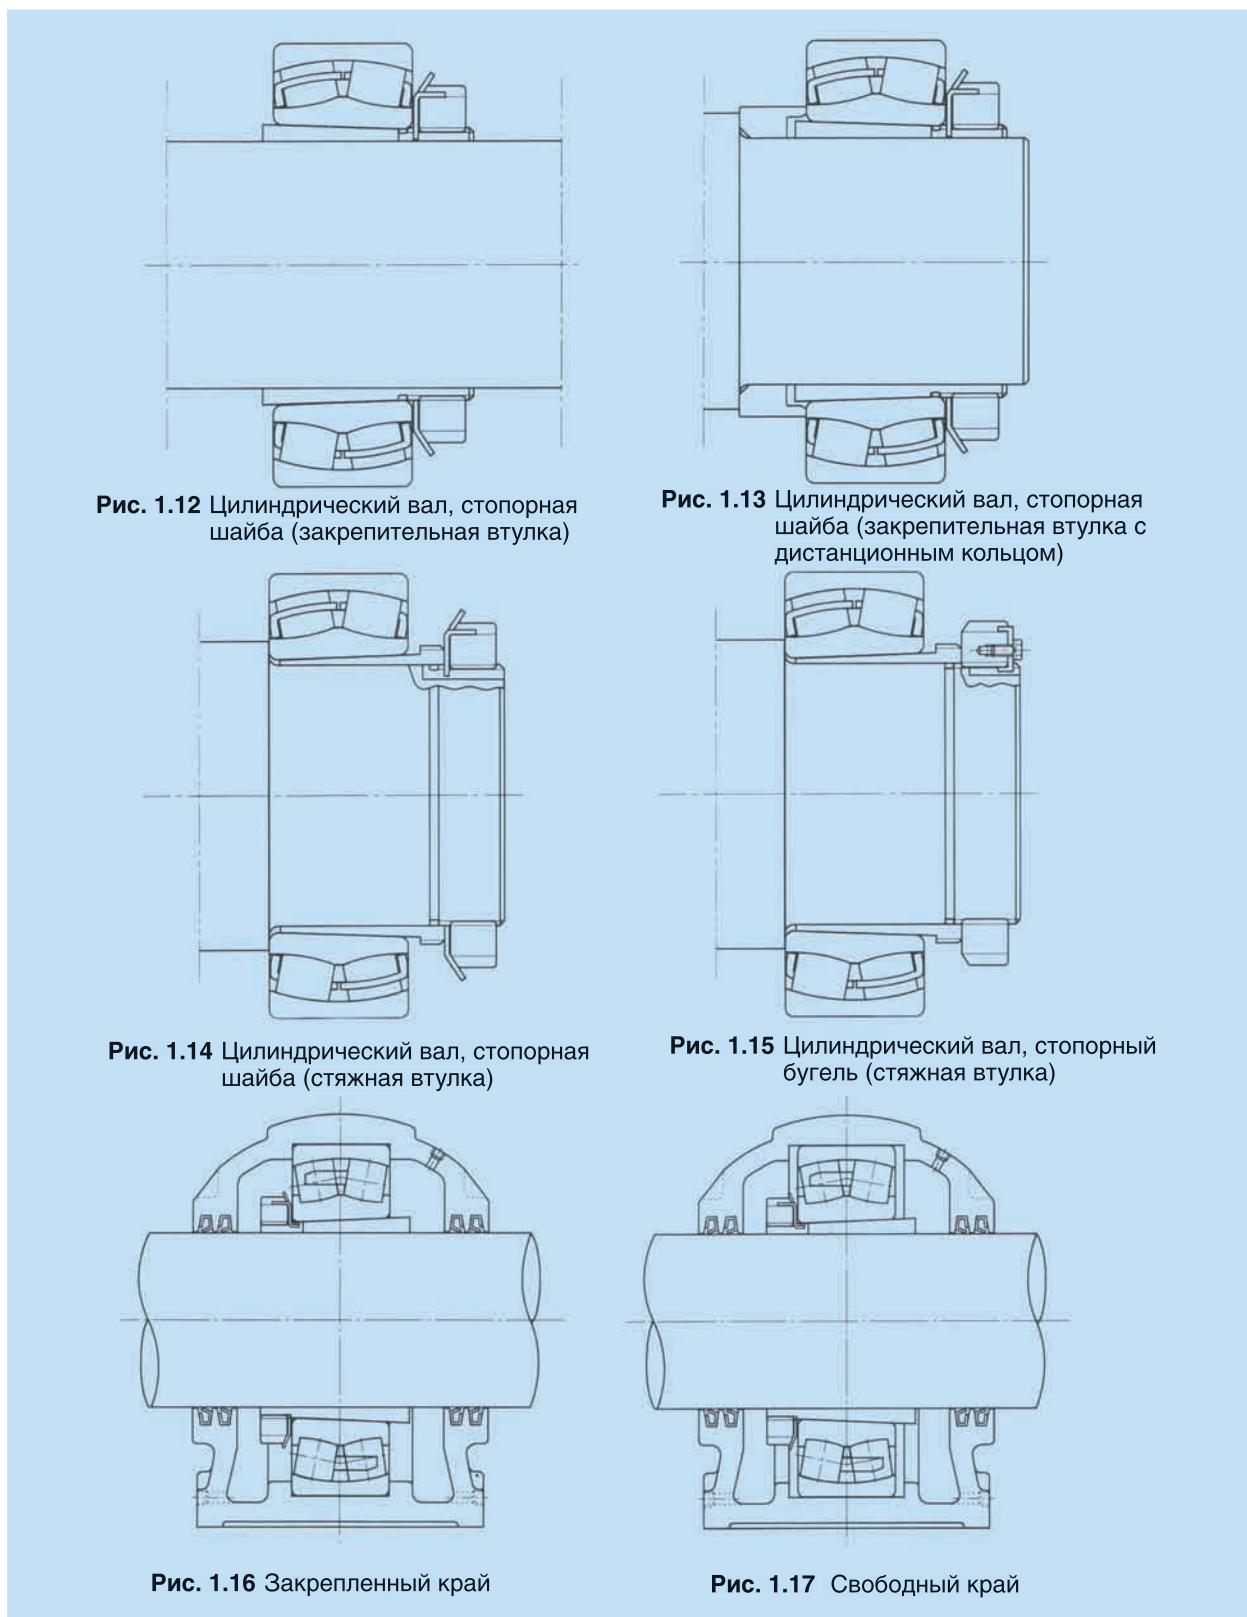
Цилиндрический вал, стопорная шайба (закрепительная втулка)
